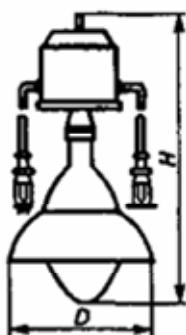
Внешний вид облучателя серии ОТ-400МИ-045
